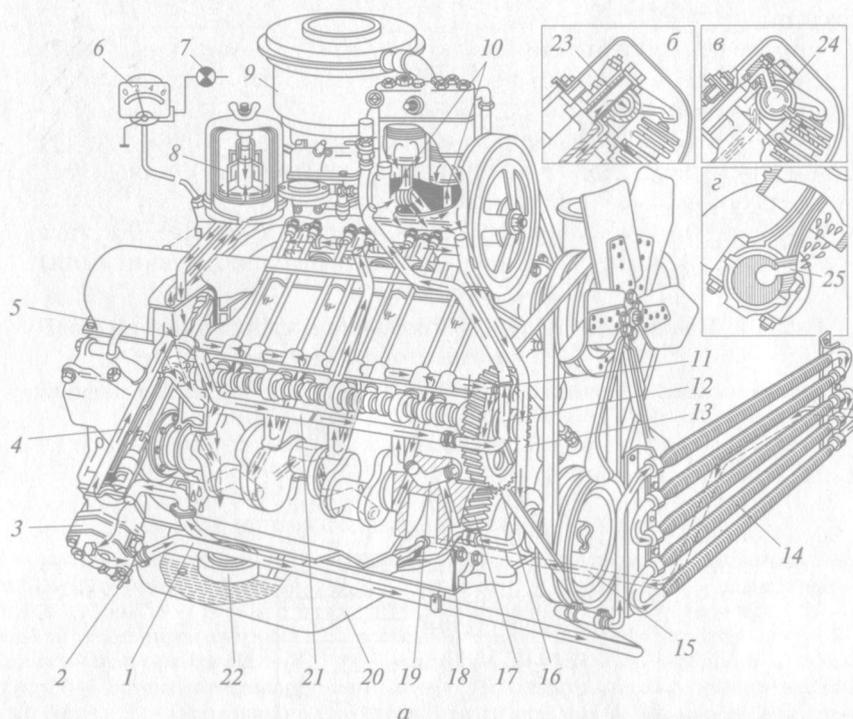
Смазочная система двигателя ЗИЛ-130:
